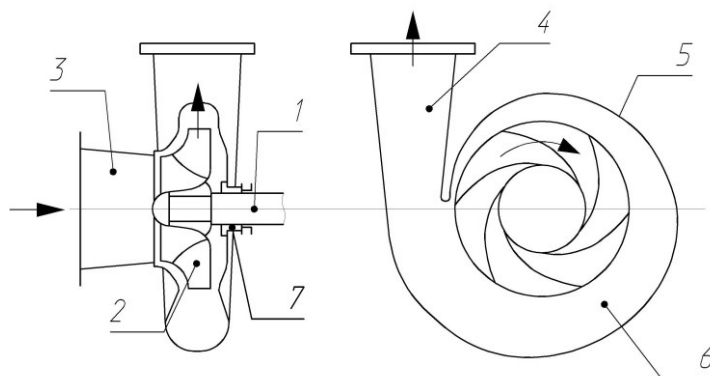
Схема центробежного насоса: 1-вал, 2 - рабочее колесо; 3 - всасывающий патрубок; 4 - напорный патрубок; 5 - корпус; 6 – спиральная камера; 7 – уплотнение вала рабочего колеса.
